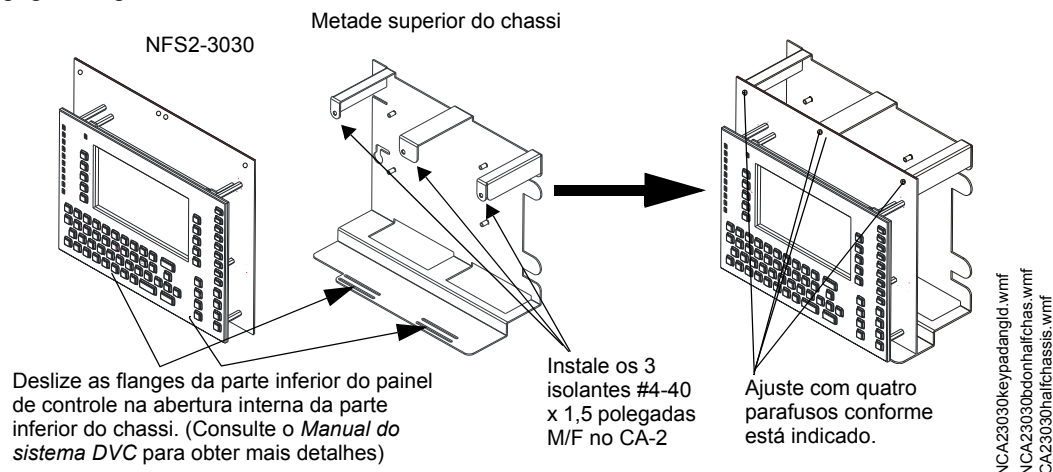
Montagem do NFS2-3030 na metade do chassi CA-2
